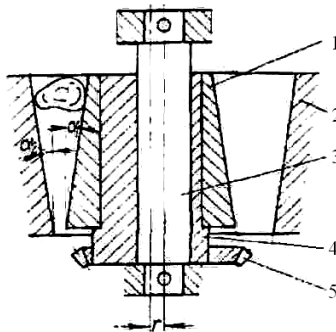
Схема конусної дробарки: 1 – рухомий конус; 2 – нерухомий конус; 3 – вісь; 4 – ексцентриковий вал; 5 – шестерня
